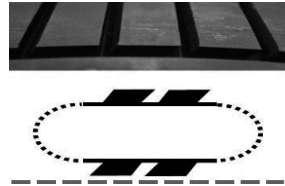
Reifenprototyp und Skizze der Seitenansicht mit geneigter Flanke
